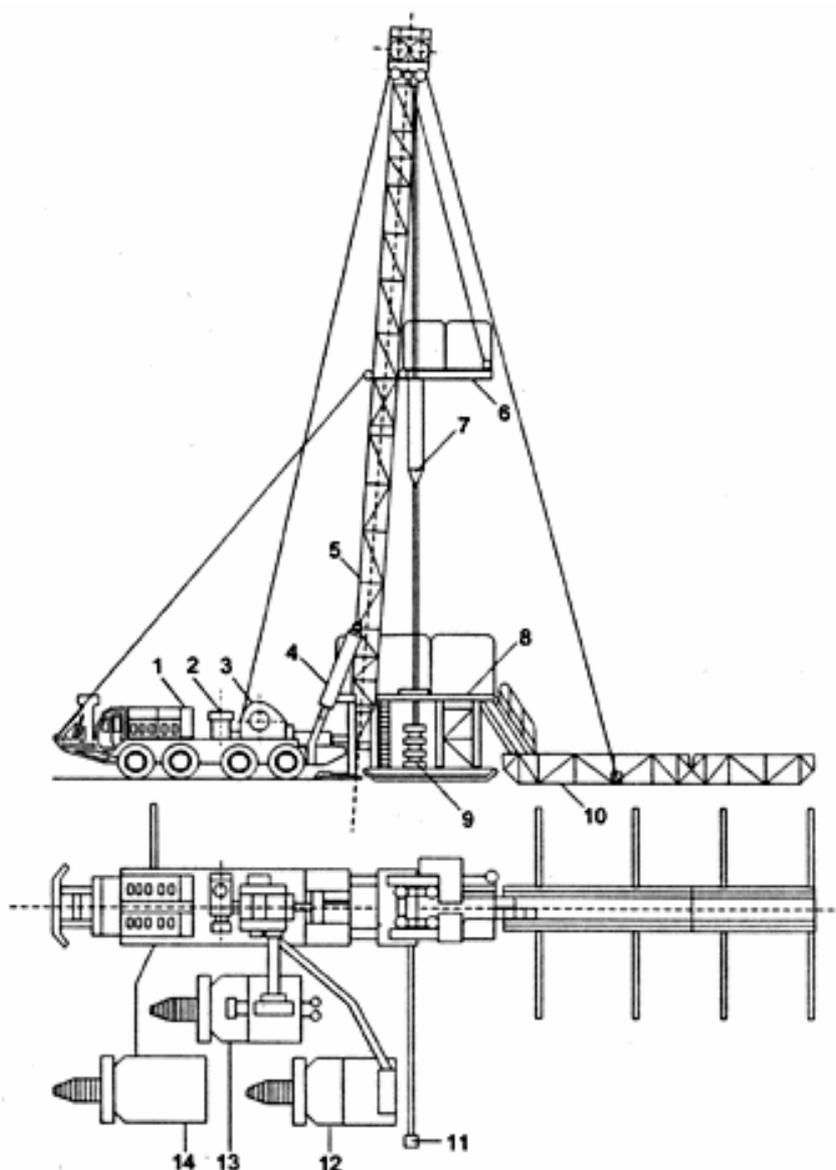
Установка КОРО 1-80 в рабочем положении
